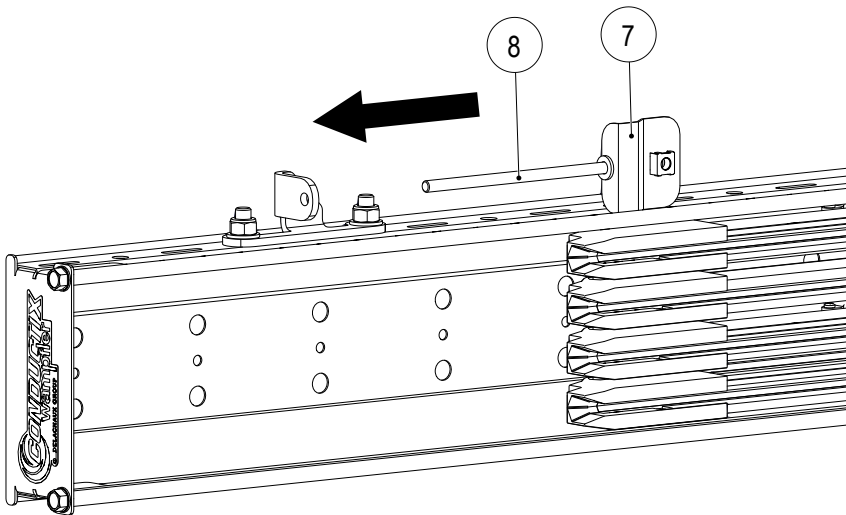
Gewindestange (8) mit Befestigungsblech der Spanneinheit (7) in den Halter schieben
